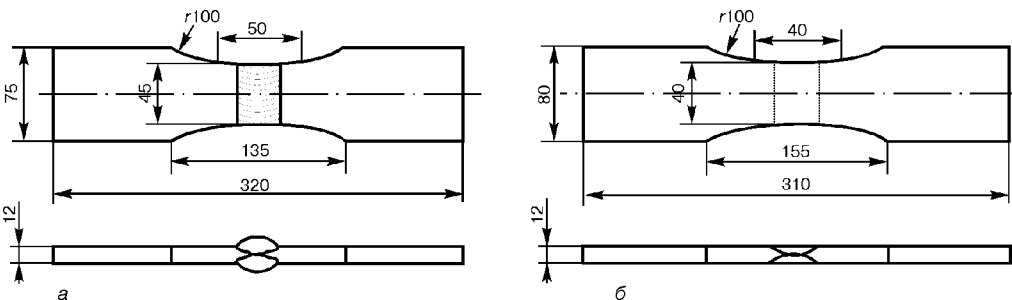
Образцы стыковых сварных соединений в исходном состоянии после сварки без обработки (а), со снятой выпуклостью шва, а также после высокочастотной проковки (б)
